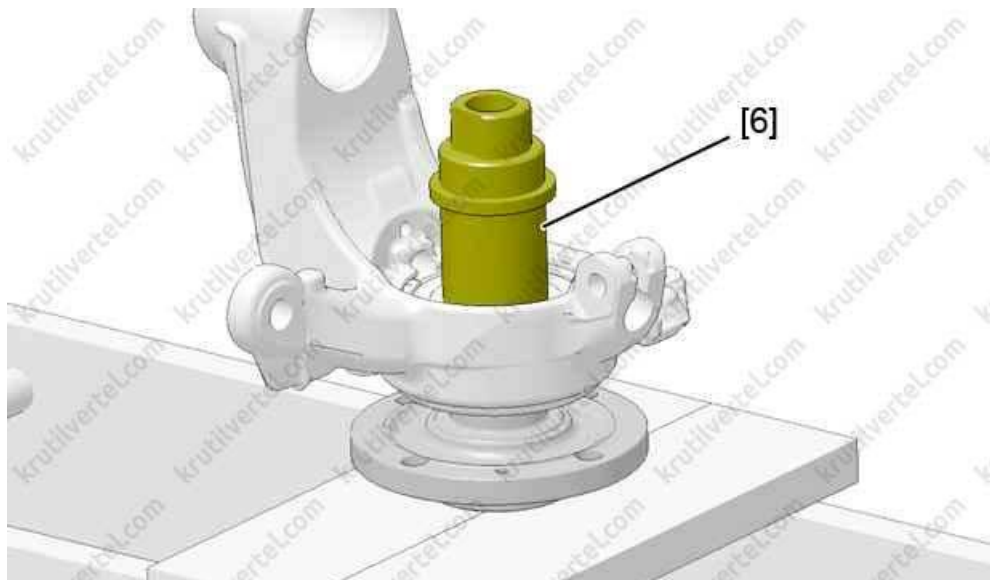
Запресування маточини в поворотний кулак:
